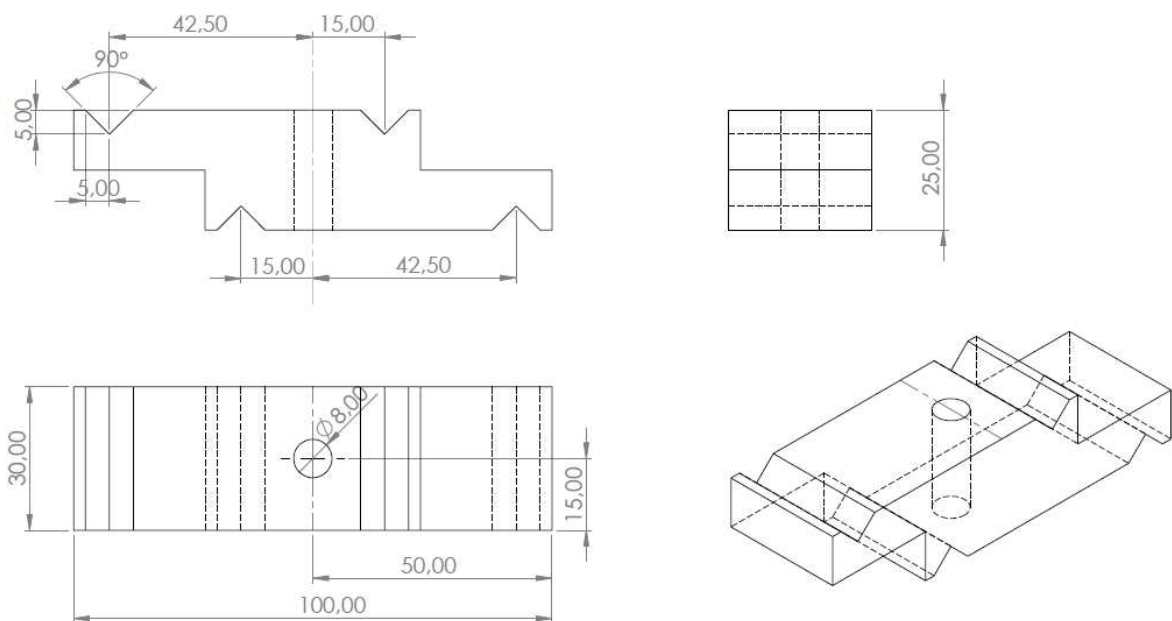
dima di allineamento per 4PB asimmetrico, disegni CAD
